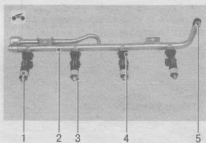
Топливная рампа и форсунки: 1 — форсунка; 2 — топливная рампа; 3 — уплотнительное кольцо; 4 — фиксатор форсунок; 5 — клапанчик штуцера для контроля давления топлива
